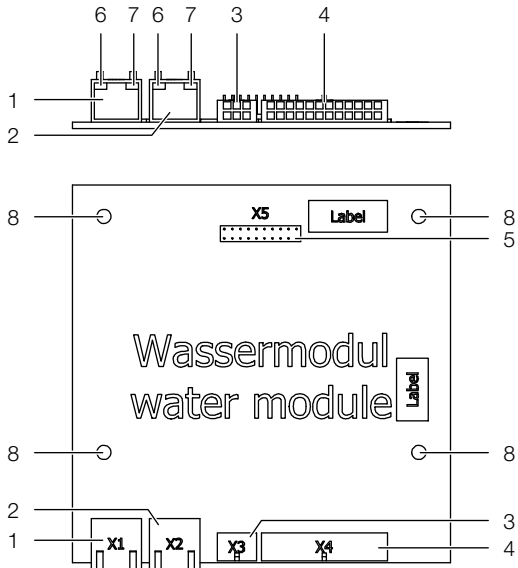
unité de régulation module hydraulique – face arrière/
